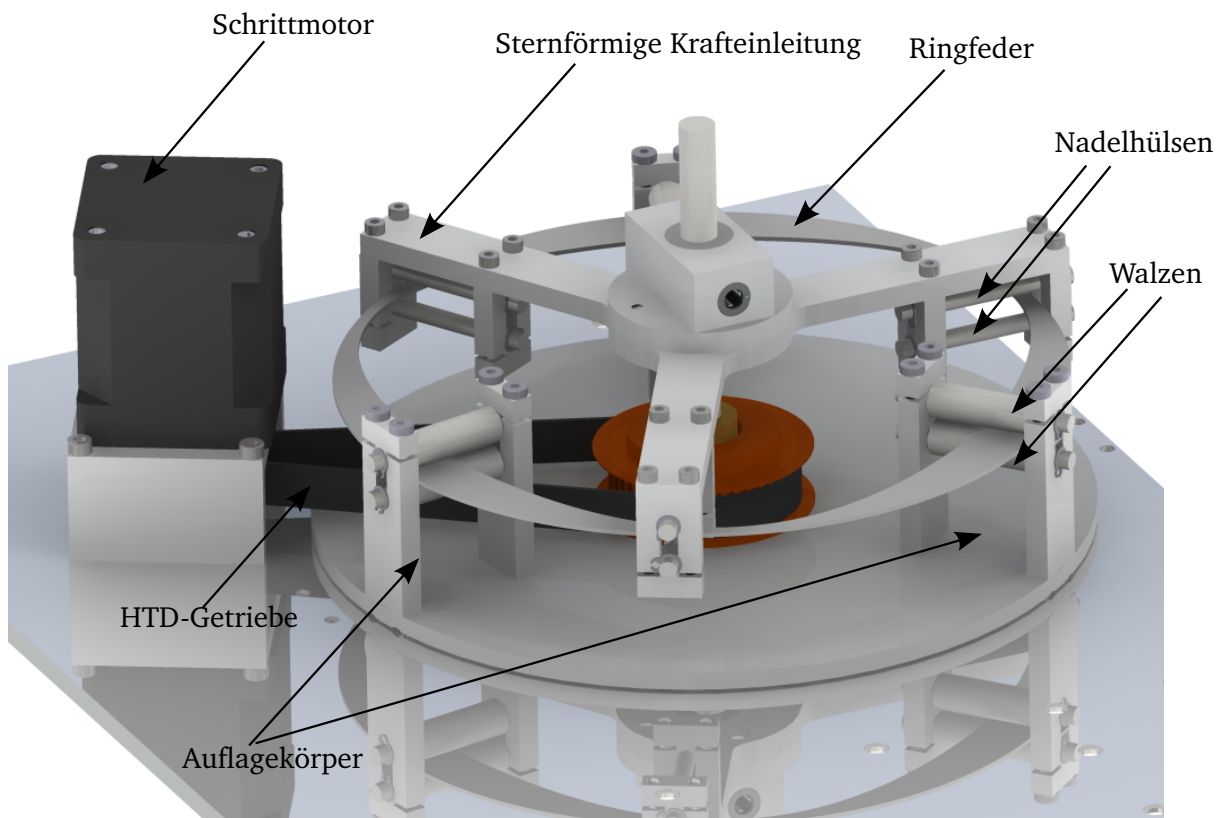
CAD-Zeichnung der Federbaugruppe
